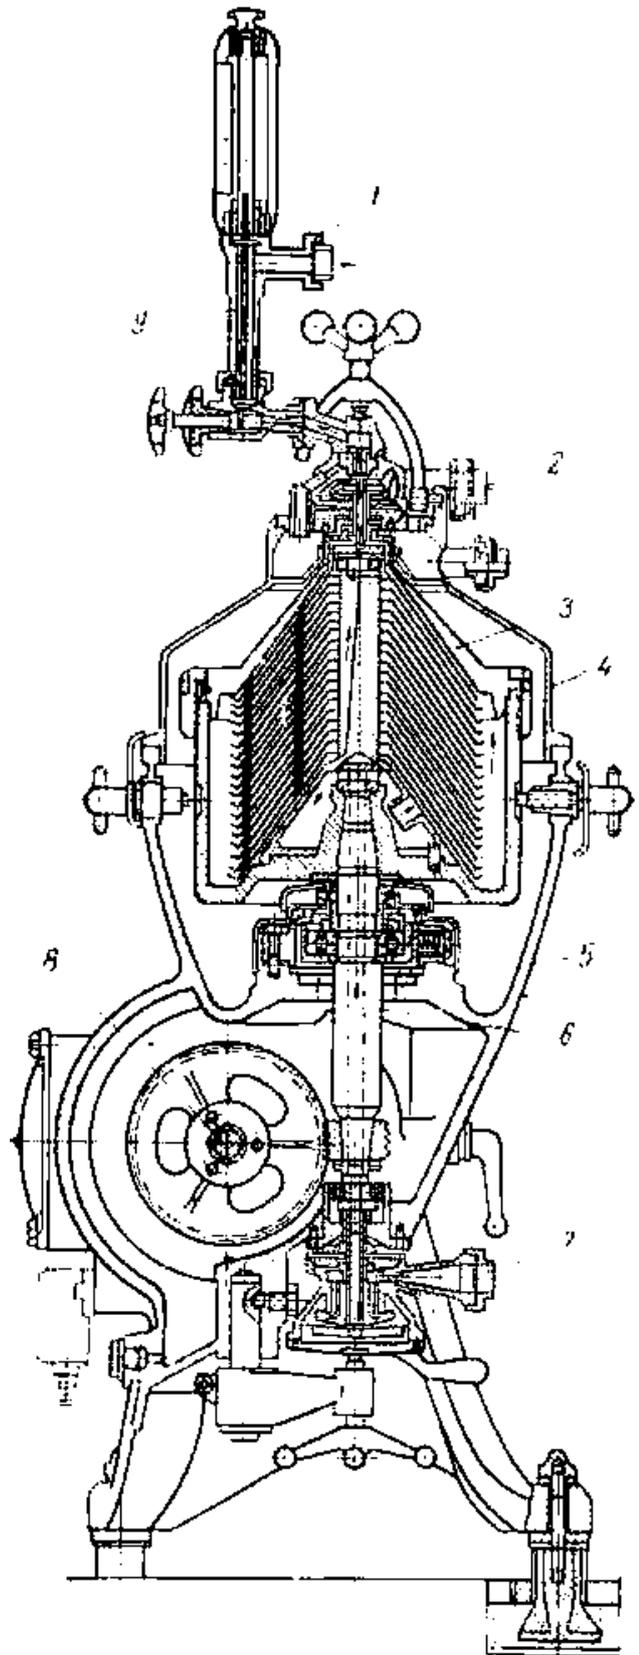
Герметический сепаратор: 1- патрубок для выхода сливок; 2 - патрубок для выхода обезжиренного молока; 3 - барабан; 4 - колпак; 5 - станина; 6 - вертикальный вал; 7 - устройство для входа молоко; 8 - горизонтальный вал; 9 - сливкомер
